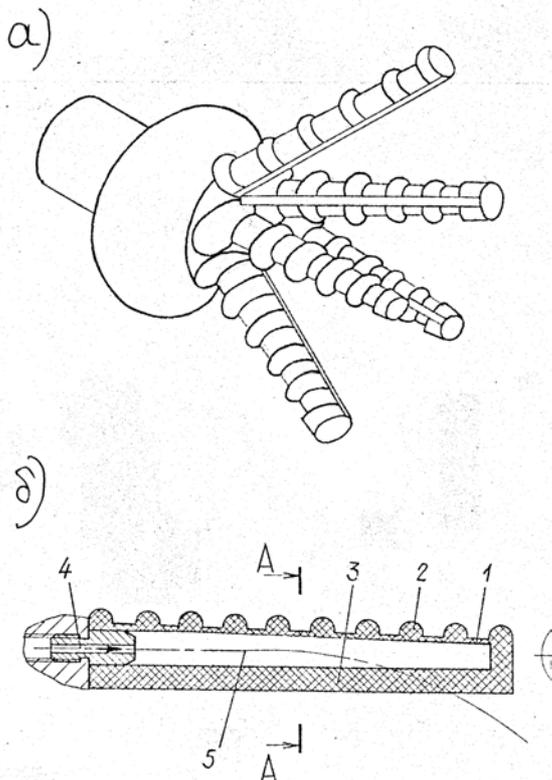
Пневматический схват с пятью гибкими надувными пальцами: а – внешний вид; б – разрез пальца:
